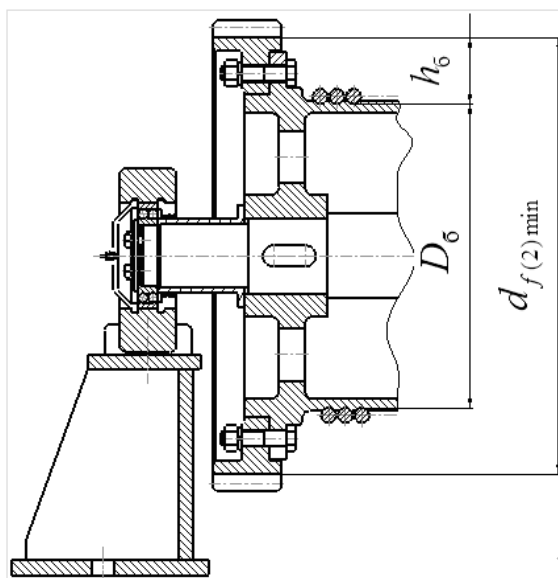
Компонировочная схема привода барабана с открытой передачей
